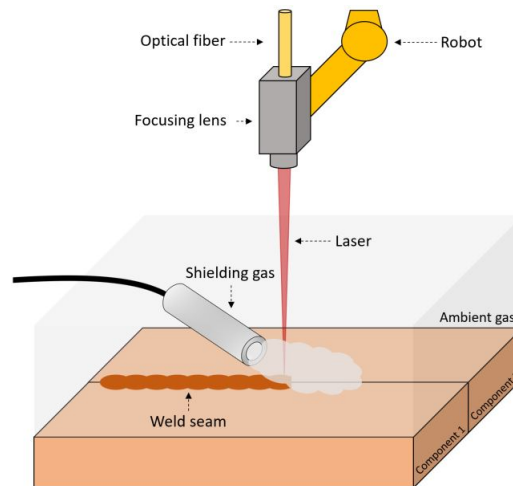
Illustration d'une installation de soudage laser.
